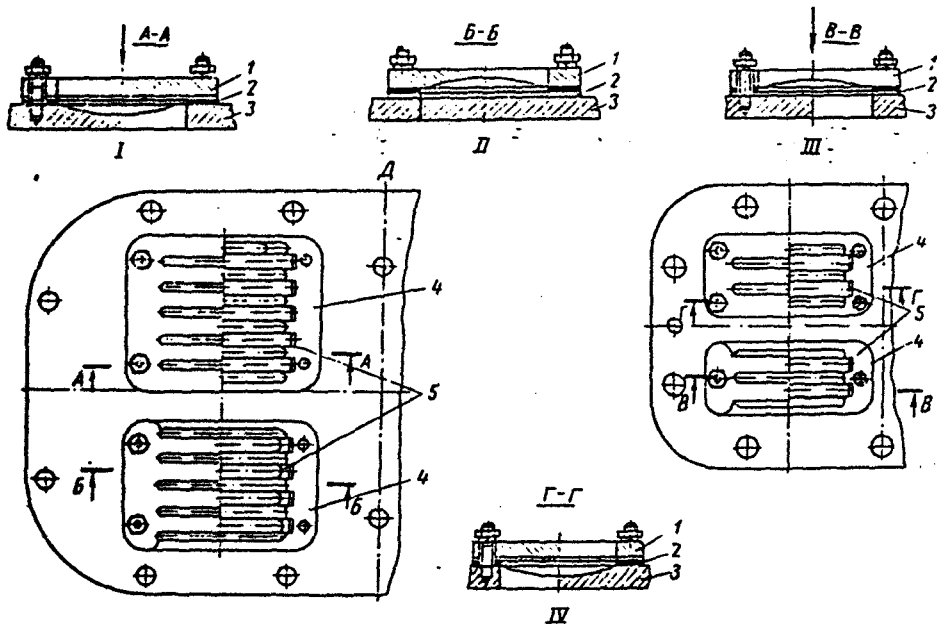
Клапаны I и II ступеней компрессора К-5М:
